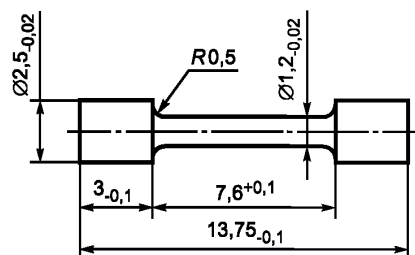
Образец для испытаний на статическое растяжение диаметром рабочей части 1,2 мм
